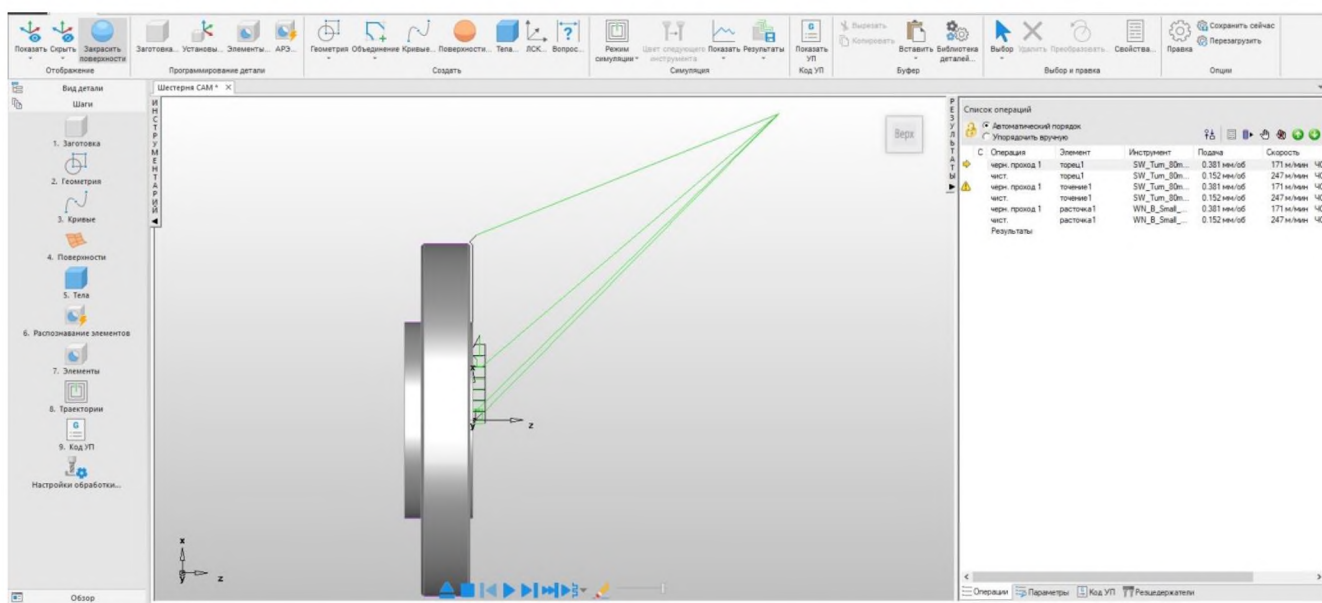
Заготовка деталі «Шестерня» у FeatureCAM з траєкторією руху інструменту та етапами обробки
